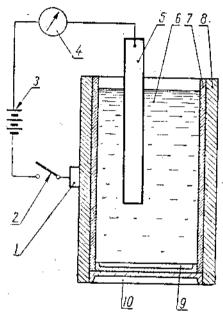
Приспособление для проверки качества сварных швов электролитическим способом.
